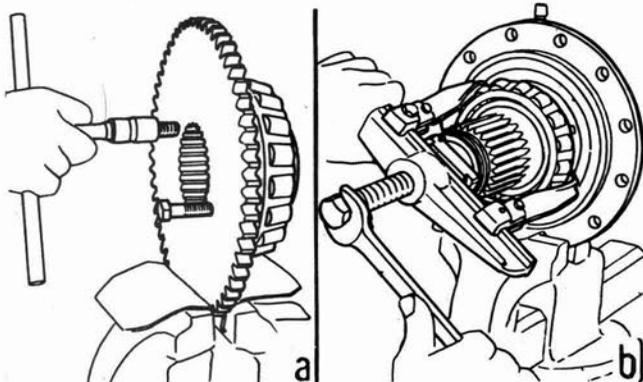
Démontage des roulements de l'engrenage fixe (a) de la fusée (b) au moyen de deux vis d'extraction (M 8 x 1,25) et d'un extracteur universel.
